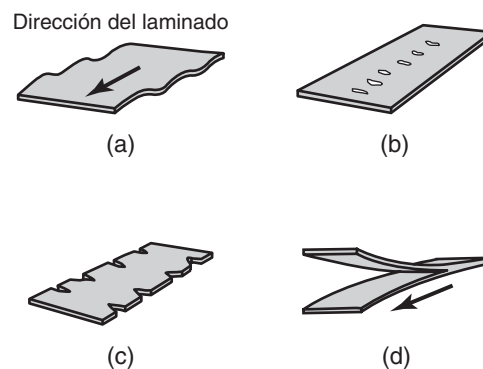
Esquema de defectos típicos en laminación plana: (a) bordes ondulados; (b) grietas en forma de cremallera en el centro de la cinta; (c) grietas de los bordes y (d) acocodrilado.
